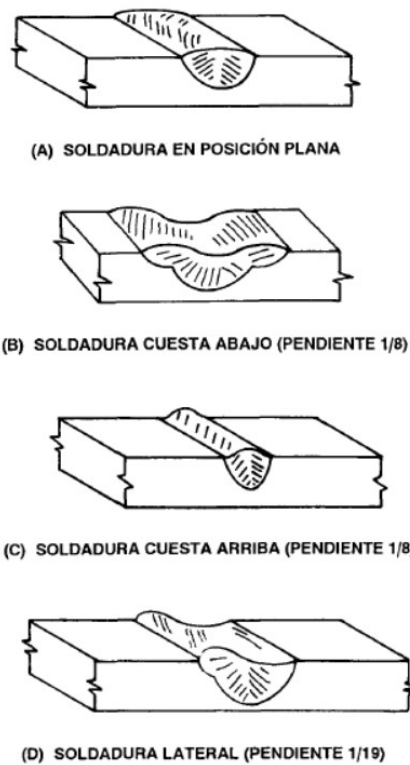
Efecto de la inclinación de la pieza de trabajo sobre la geometría del cordón de soldadura (4).
